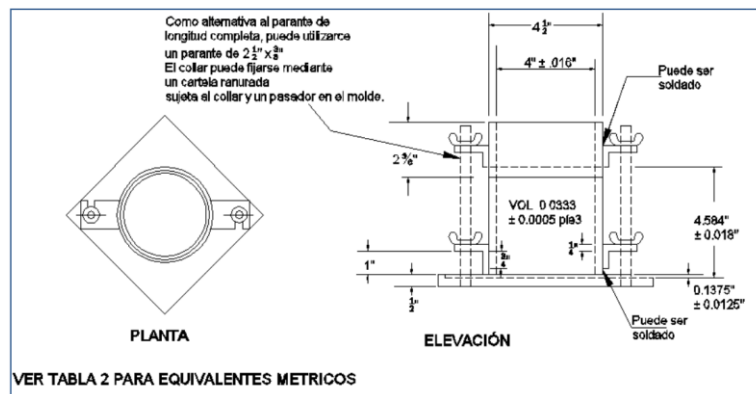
Molde Cilíndrico de 4". Fuente: [32]
